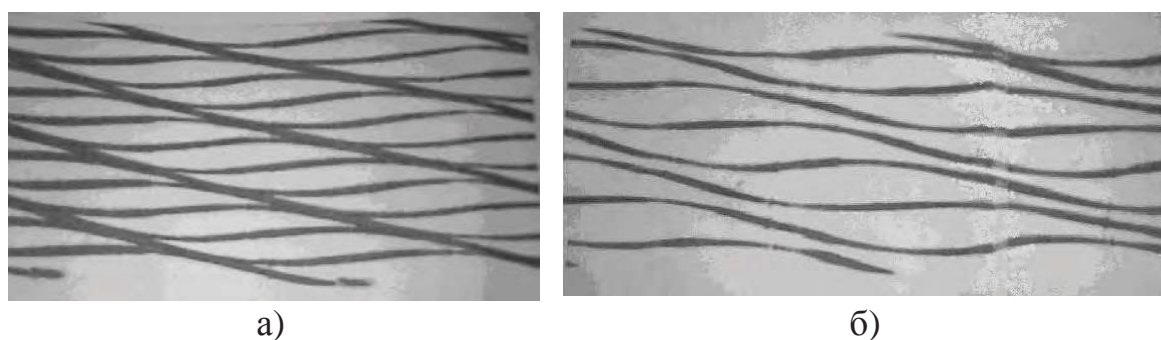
Фото траектории следов перемещения точки контакта инструмента по обрабатываемой поверхности
